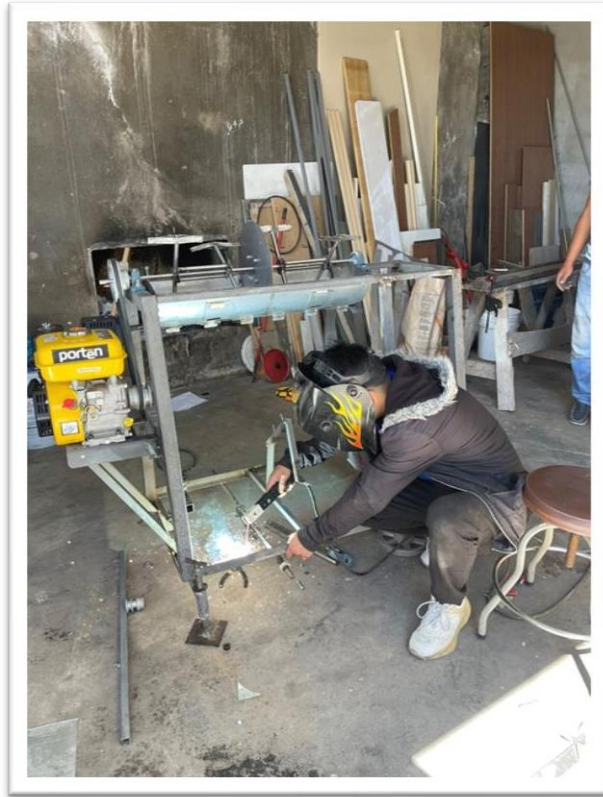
Proceso de Soldadura en la Fabricación y Ensamblaje de la Máquina.
